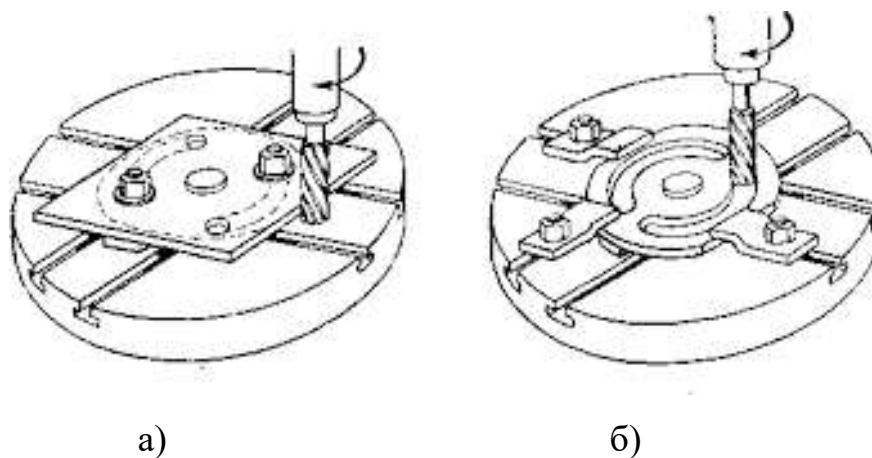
Приклад контурного фрезерування: а – зовнішньої криволінійної поверхні бічною поверхнею фрези; б – внутрішньої криволінійної поверхні бічною поверхнею та торцем фрези.
